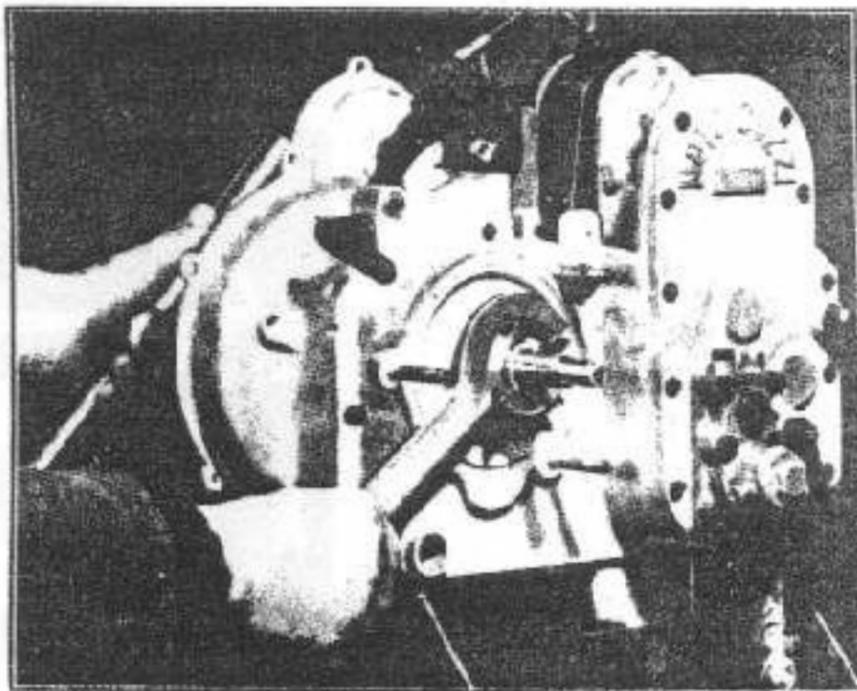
Come si smonta la ghiera di serraggio del pignone del cambio.
